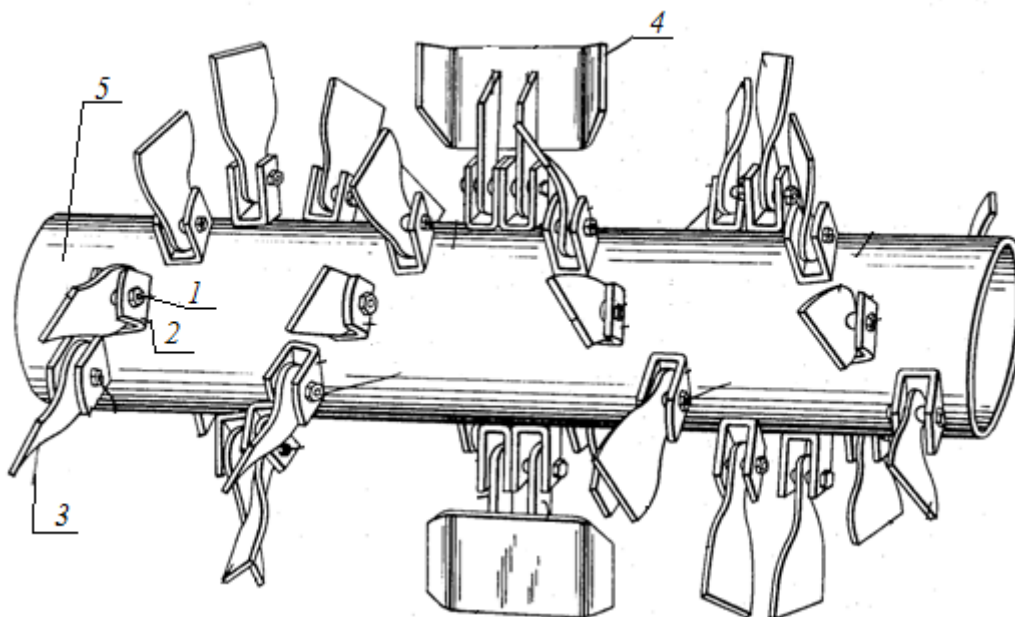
Общий вид снегоочистителя, где 1 – штифт; 2 - U-образная скоба; 3 – цепной элемент; 4 – метательное лезвие; 5 – корпус шнека
